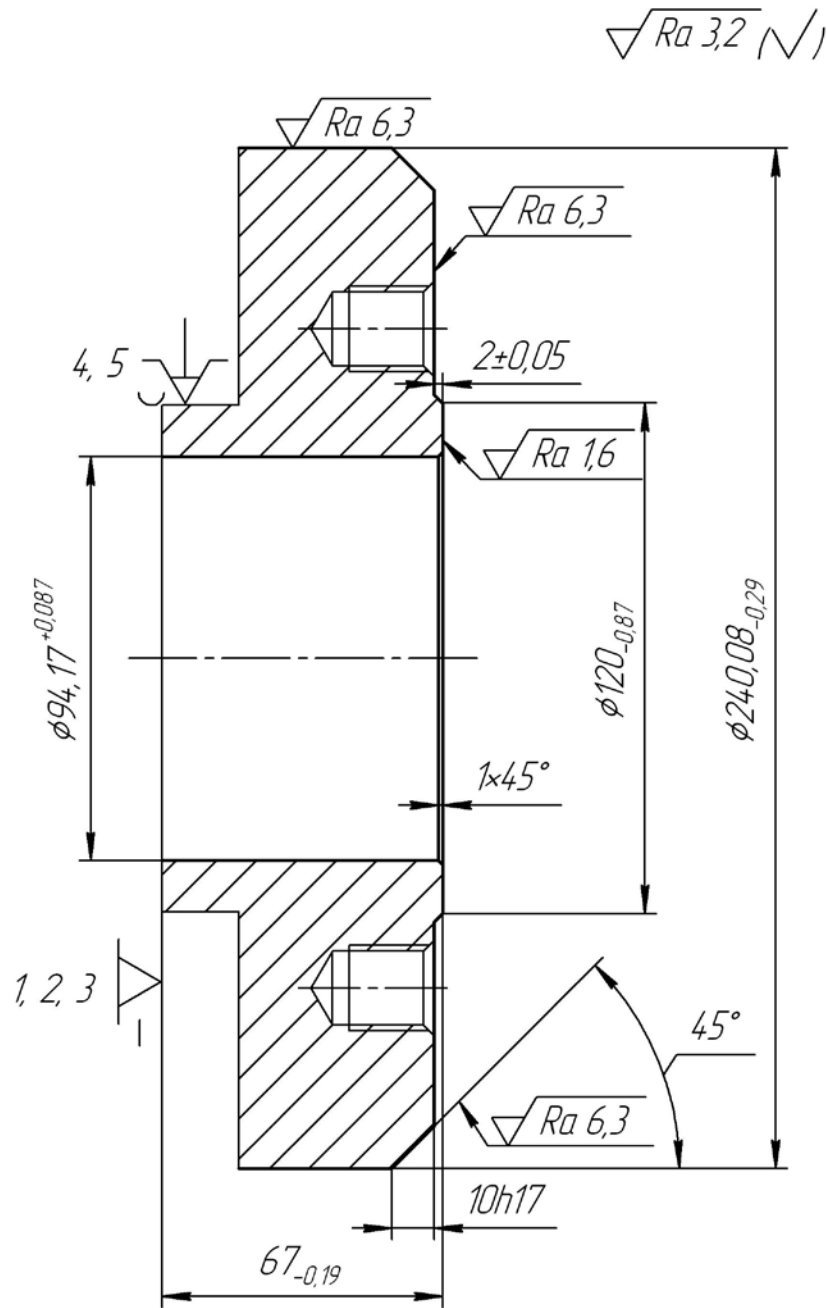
Схема базування заготовки на операції 045 токарній з ЧПК
